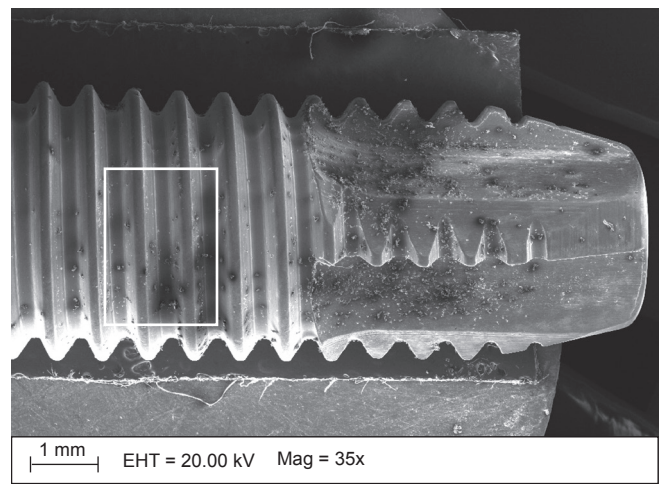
Implantes cilíndricos com superfície usinada após ensaio de tração.
